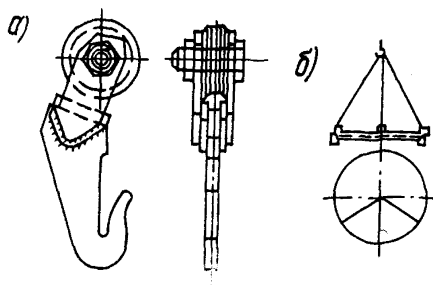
Тросовый захват для транспортировки днищ и резервуаров:
